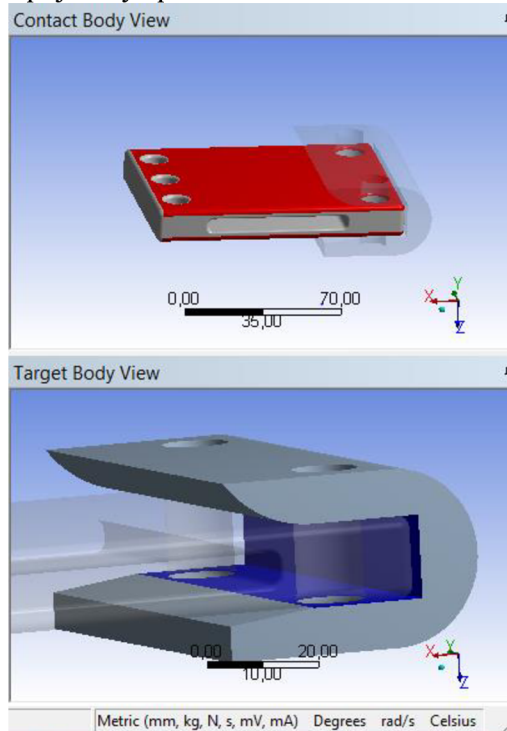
Lokálny súradnicový systém priradený k telesu planžetky
